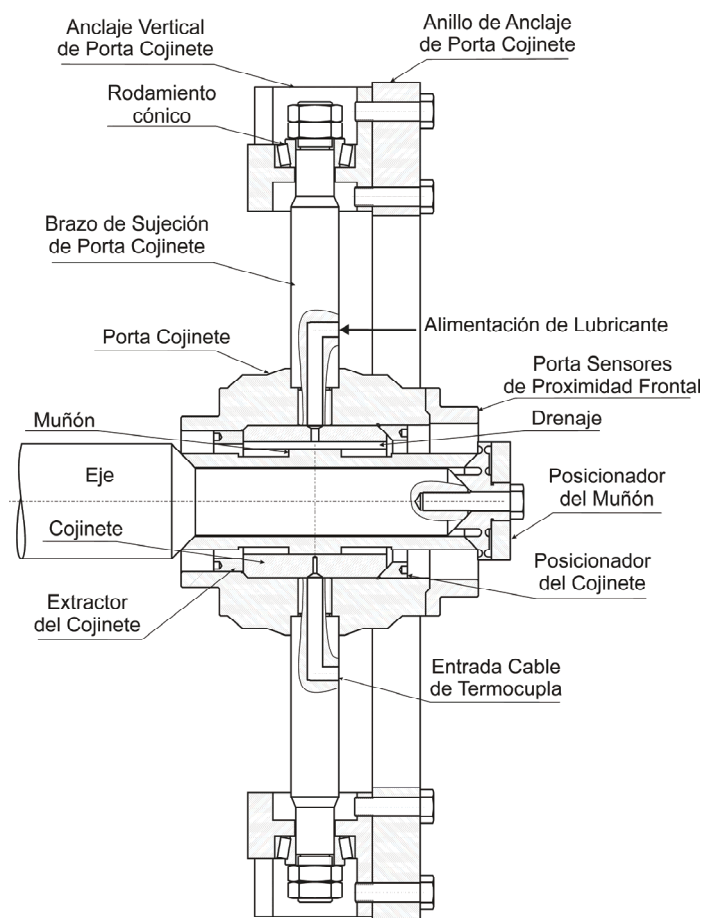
Esquema en corte del cojinete posicionado en el porta cojinete
